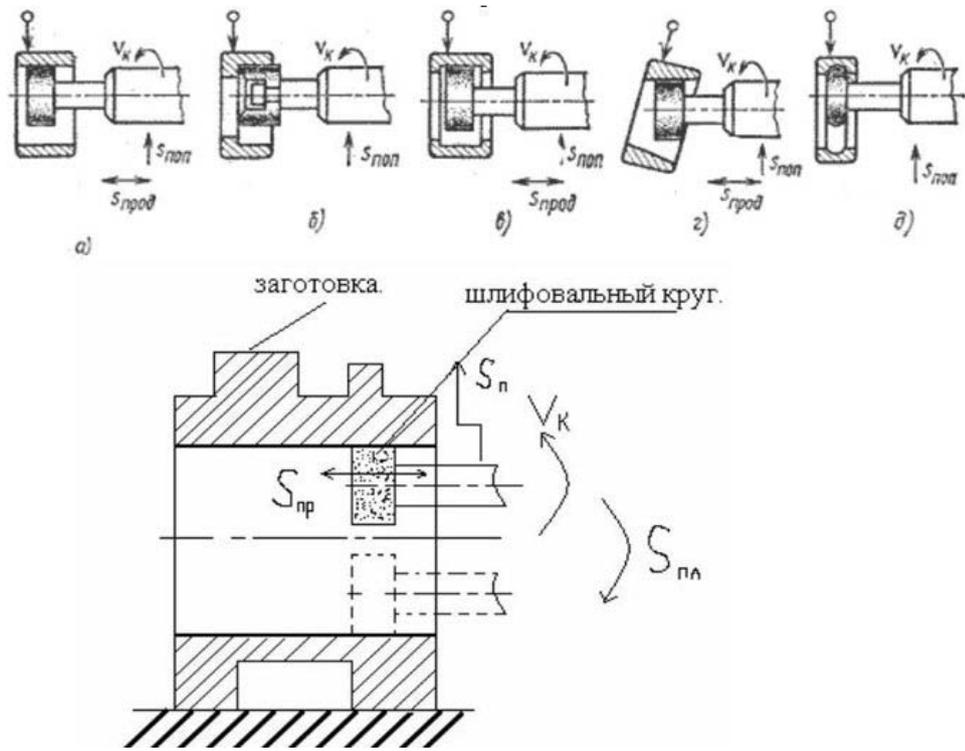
Схема планетарного шлифования отверстия и схемы шлифования отверстий во вращающихся заготовках; а – гладкого цилиндрического отверстия; б – ступенчатого отверстия и торца; в – широкой канавки; г – конического отверстия; д – фасонного паза
